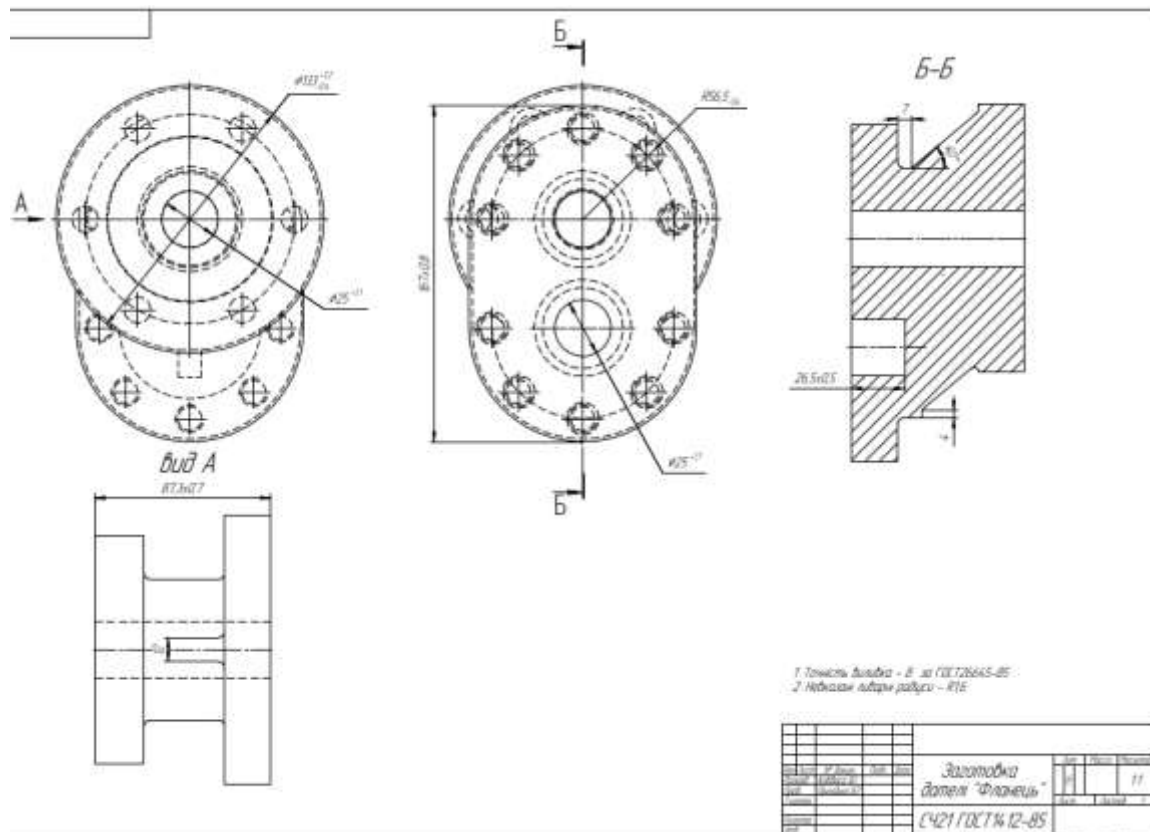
Ескіз заготовки деталі «Фланець»
